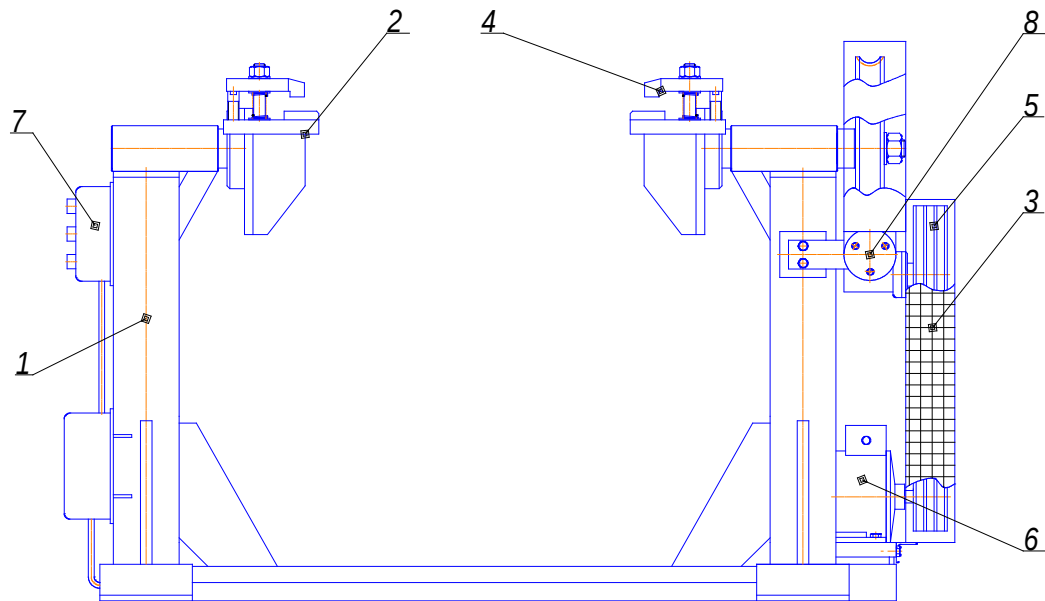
Стенд для ремонту КПП і ДВЗ: 1 – рама; 2 – затискач лівий; 3 – захисний кожух; 4 – затискач правий; 5 – передача пасова; 6 – електродвигун; 7 – станція кнопкова; 8 – редуктор черв'ячний.
